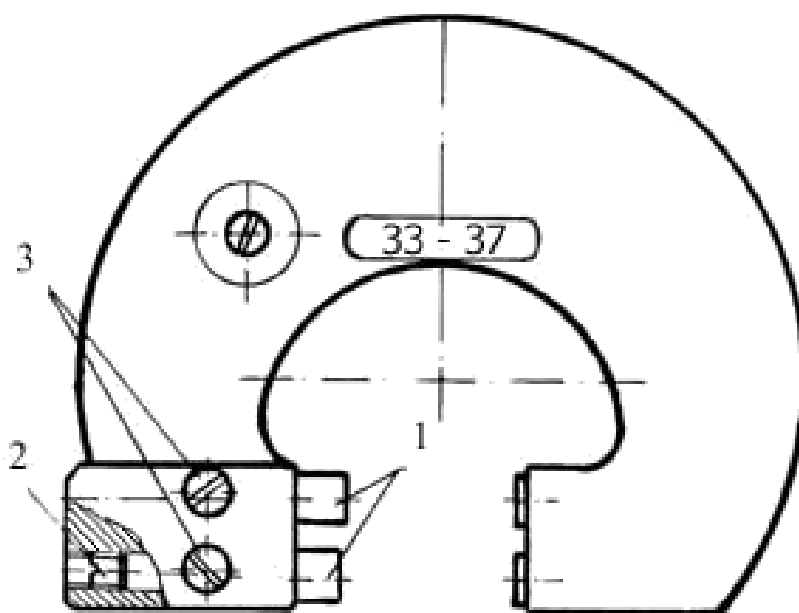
Общий вид регулируемой калибра-скобы: 1 – вставки; 2 – установочные винты; 3 – зажимные винты
